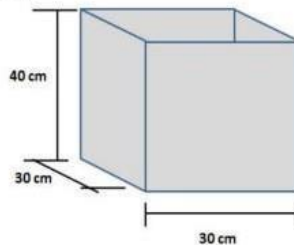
Detalhamento para plano de corte-peças 5 e 6
